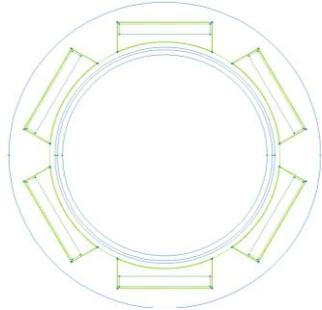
Конструкция предлагаемой установки индукционного нагрева
